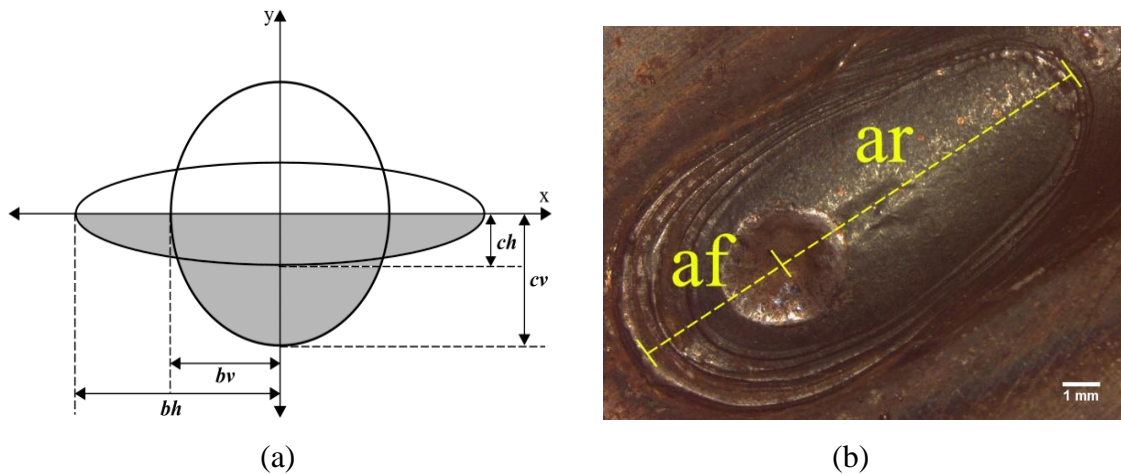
Esquema das dimensões da seção transversal de cordão de solda MAG (a); dimensões da poça de fusão MAG (b). Fonte: Autor.
